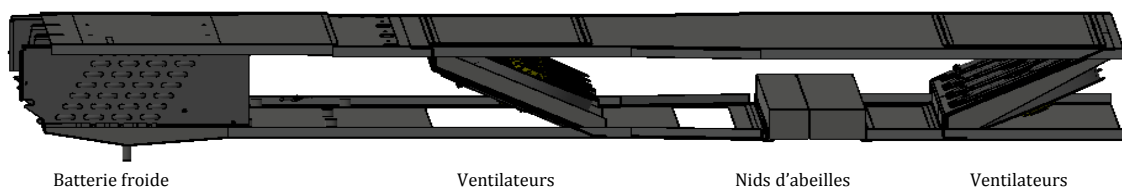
Plan 3D du dispositif de rideau d'air, vue de côté.
